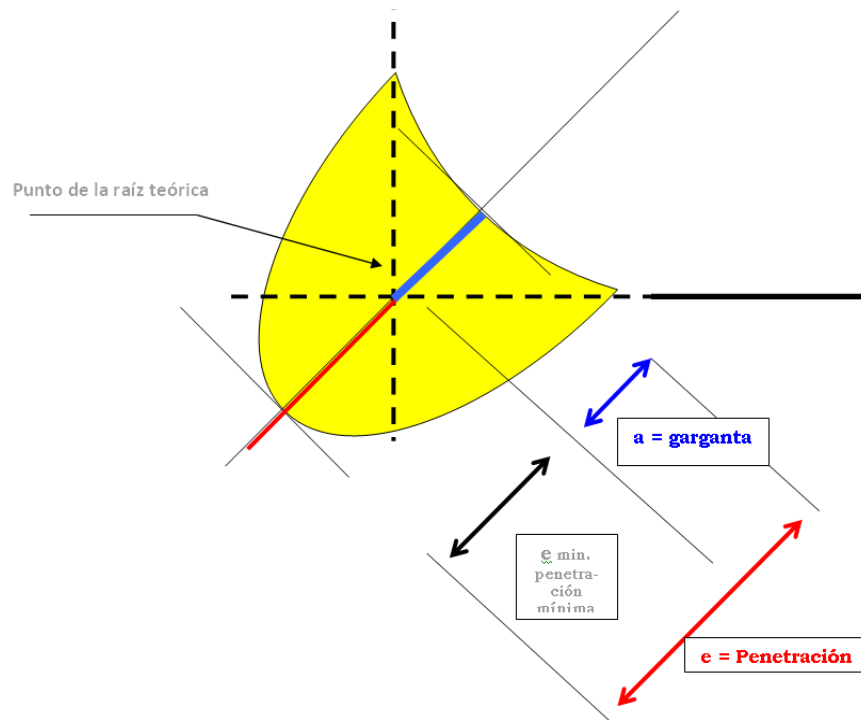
ESQUEMA DE PENETRACION DE SOLDADURA
